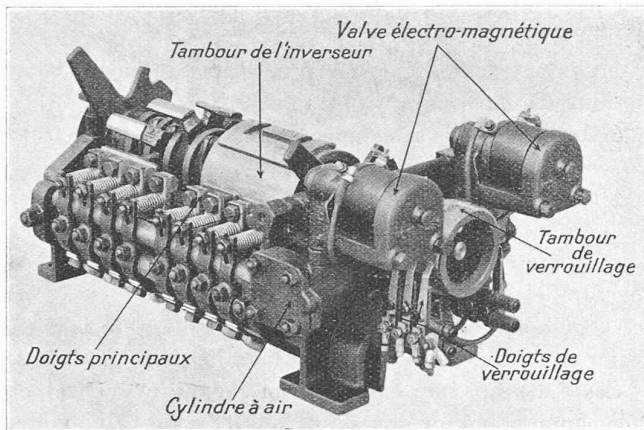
Inverseur; vue du côté des valves de commande et du tambour de verrouillage.
